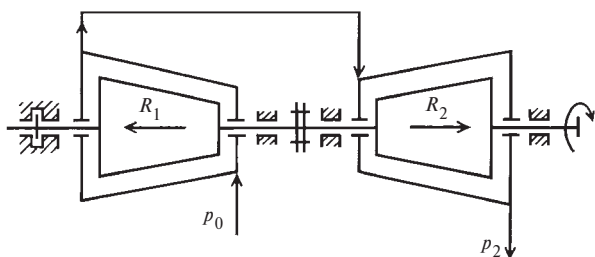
Схема разгрузки упорного подшипника в двухцилиндровой турбине
